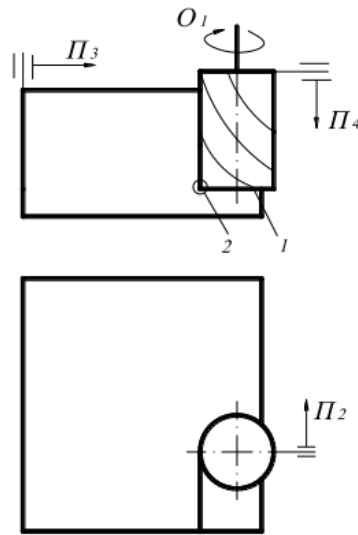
Використання кінцевої фрези при виготовленні уступу
